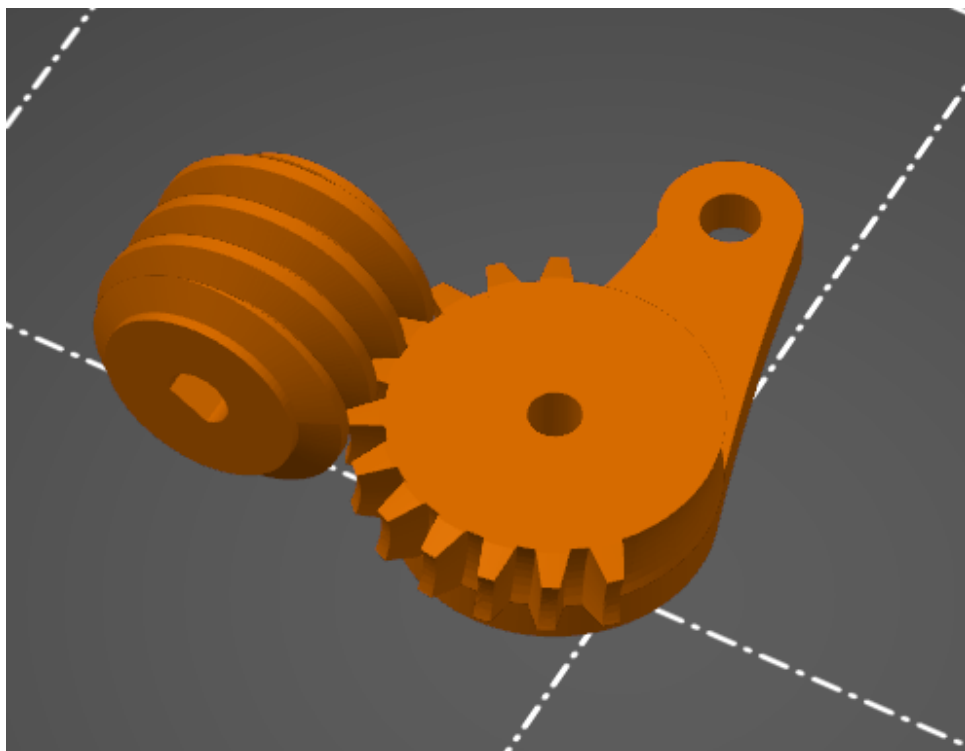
Sestrojená dlaň se šnekovým převodem
